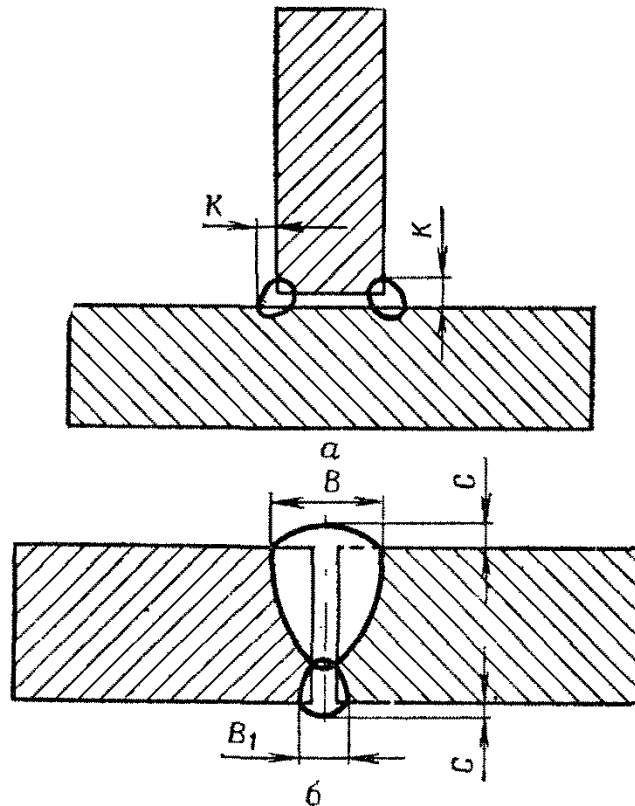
Места замеров величин элементов сварных швов:
